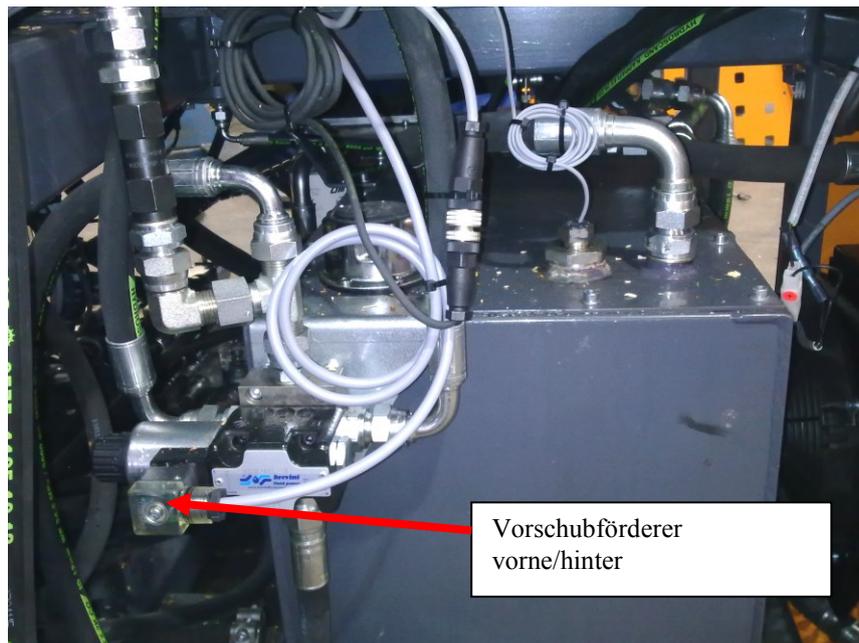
Das Wegeventil des Vorschubförderers (hinten die Maschine, befestigt in dem Öltank).
